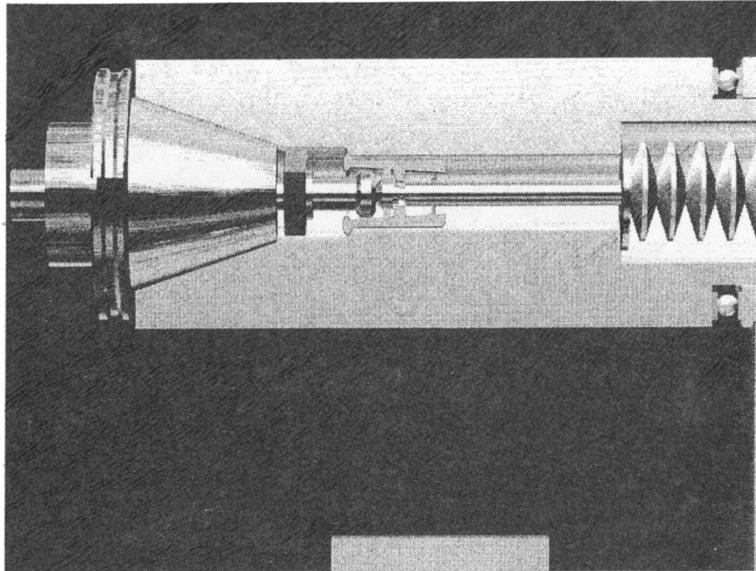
Автоматизированный зажим оправки с инструментом на фрезерном станке
